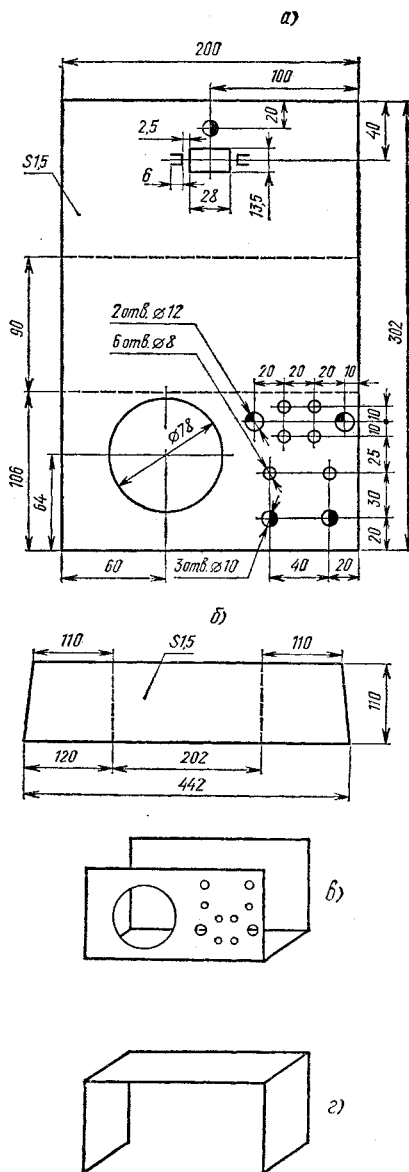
Корпус прибора: а, в — основание; б, г — крышка.
